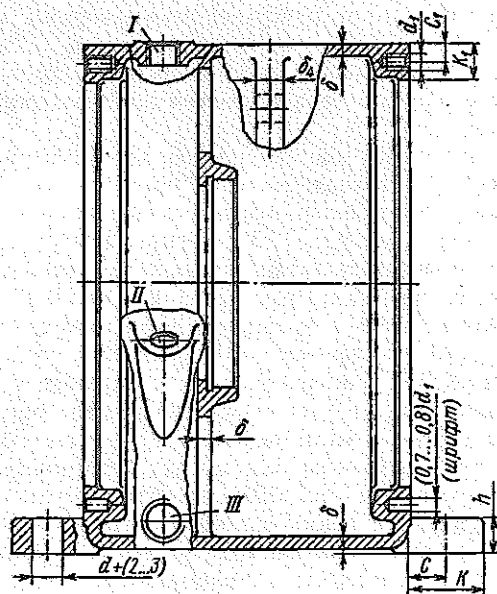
Основные элементы корпуса планетарного редуктора
